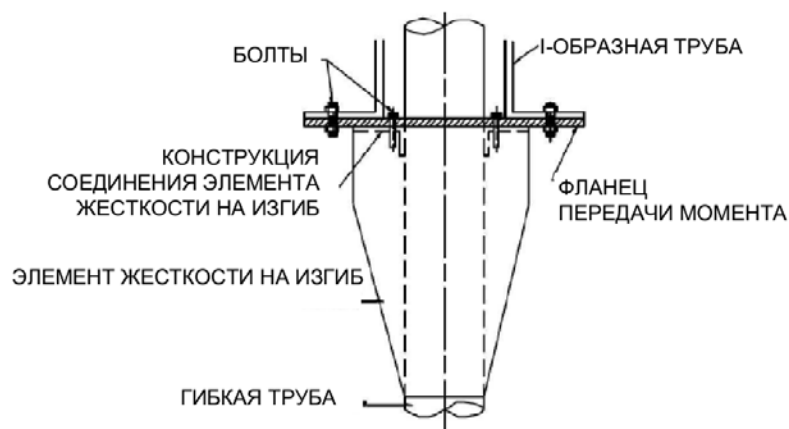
Устройство для передачи нагрузок с фланцем передачи момента
